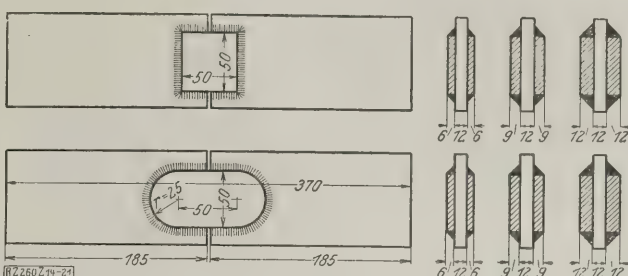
bis 21. Probestäbe mit ringsum angeschweißten Doppel-laschen.
